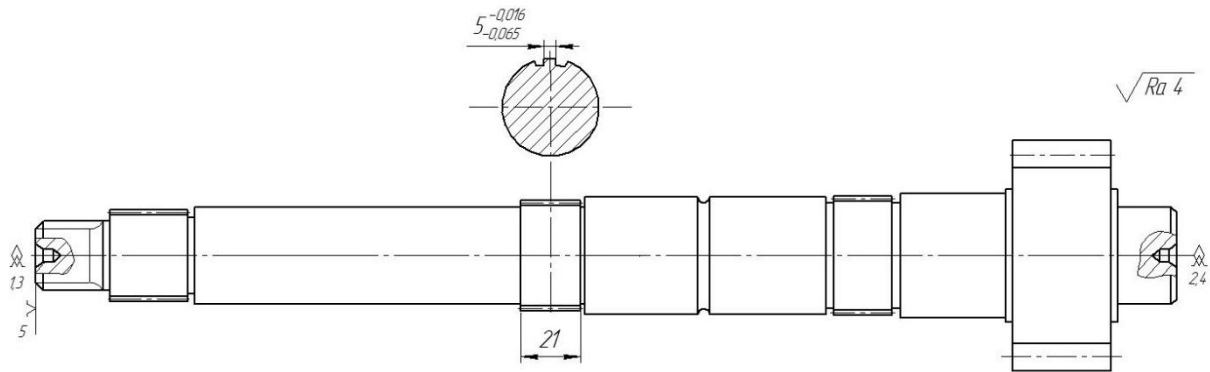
Схема встановлення вала під час фрезерного оброблення шліців.
